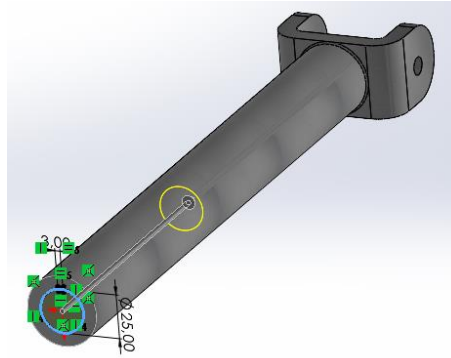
Corte árbol de transmisión deslizante de la junta cardán en SolidWorks.
